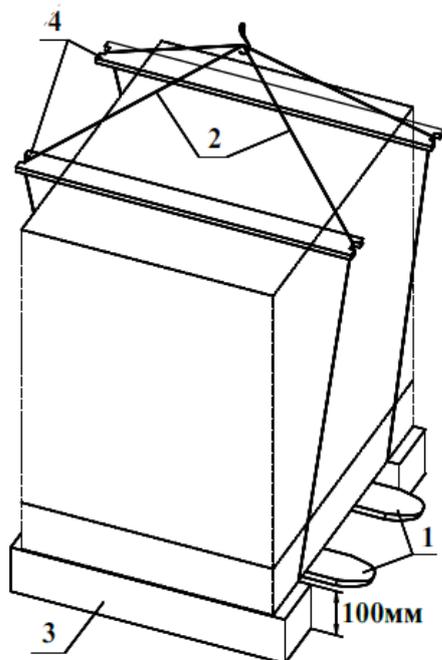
Схема строповки ККБ малых типоразмеров
